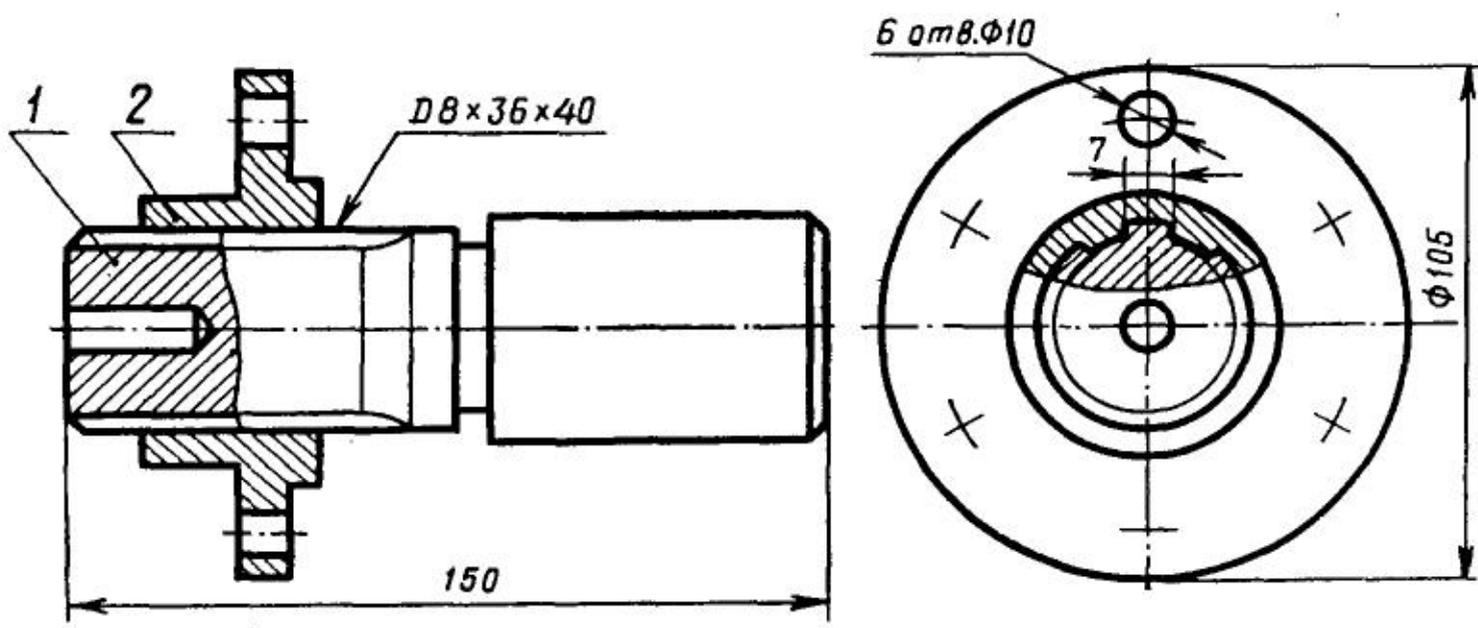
Робочі креслення деталей шліцьового з'єднання.
